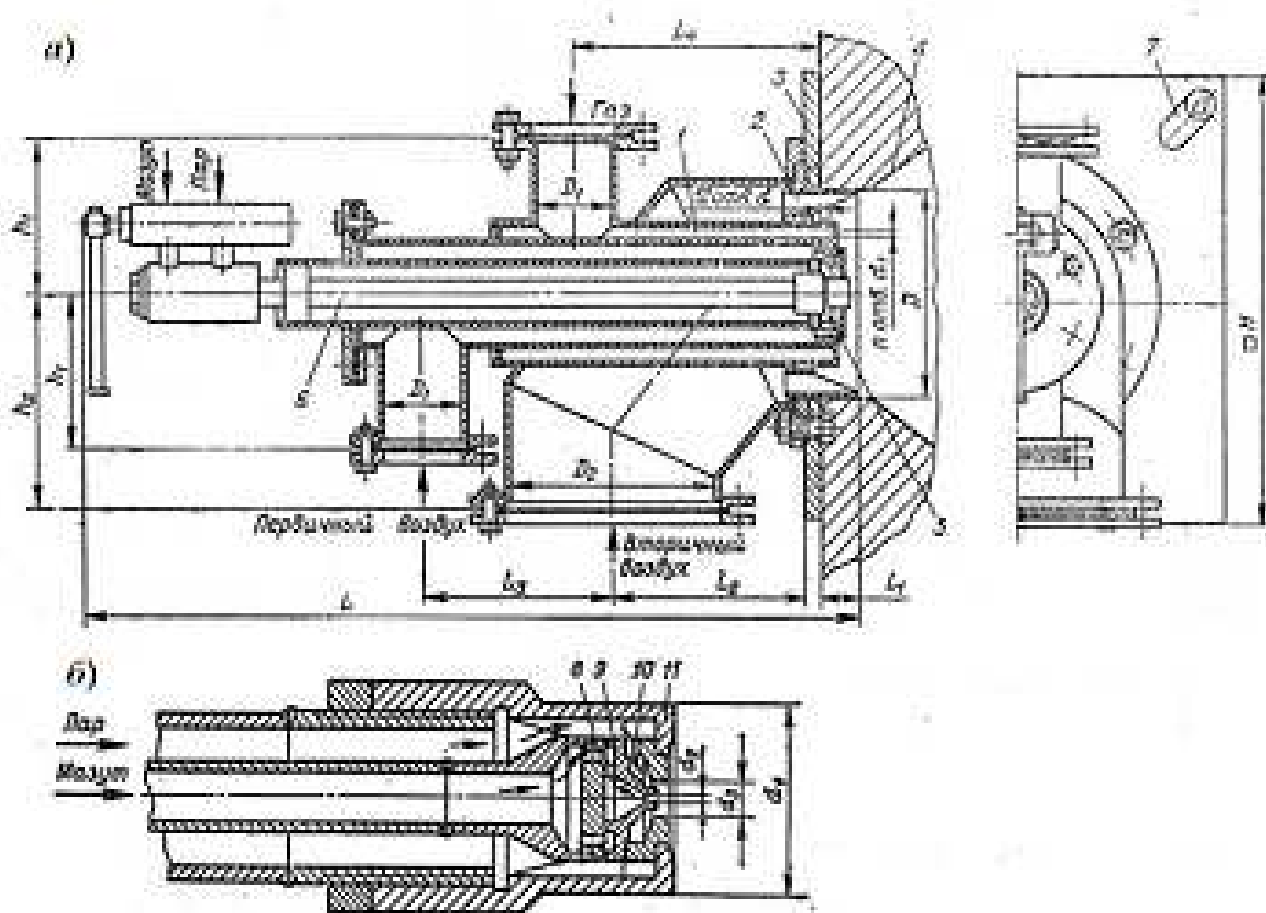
Устройство газомазутной горелки ГМГм:
